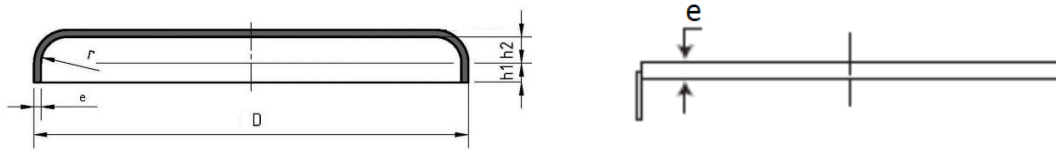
Fundo plano rebordado (a) [13] e fundo simplesmente plano (b)
